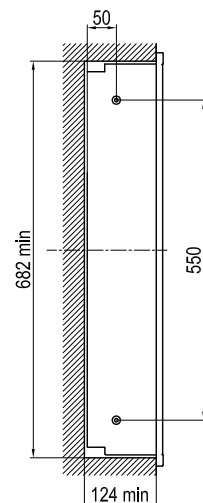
Габаритные и установочные размеры металлокорпусов
